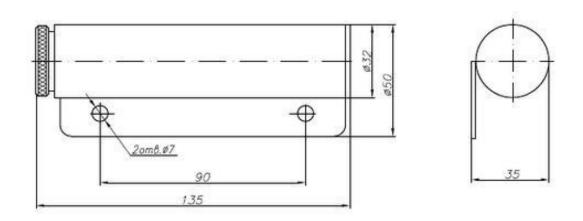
Габаритные и присоединительные размеры капсулы с магнитом.
